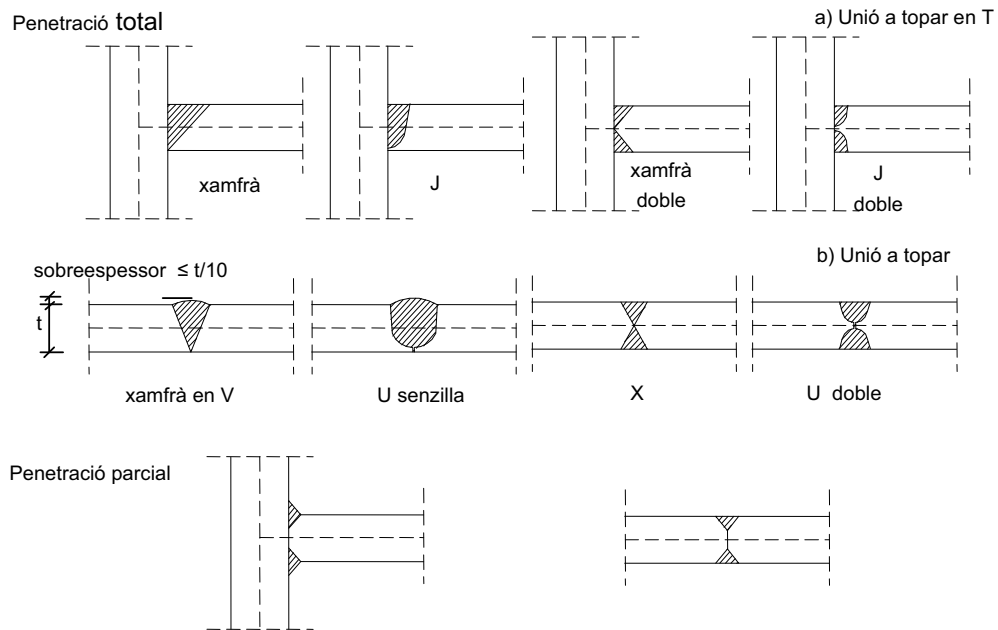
Soldadura a topar i formes de preparació
